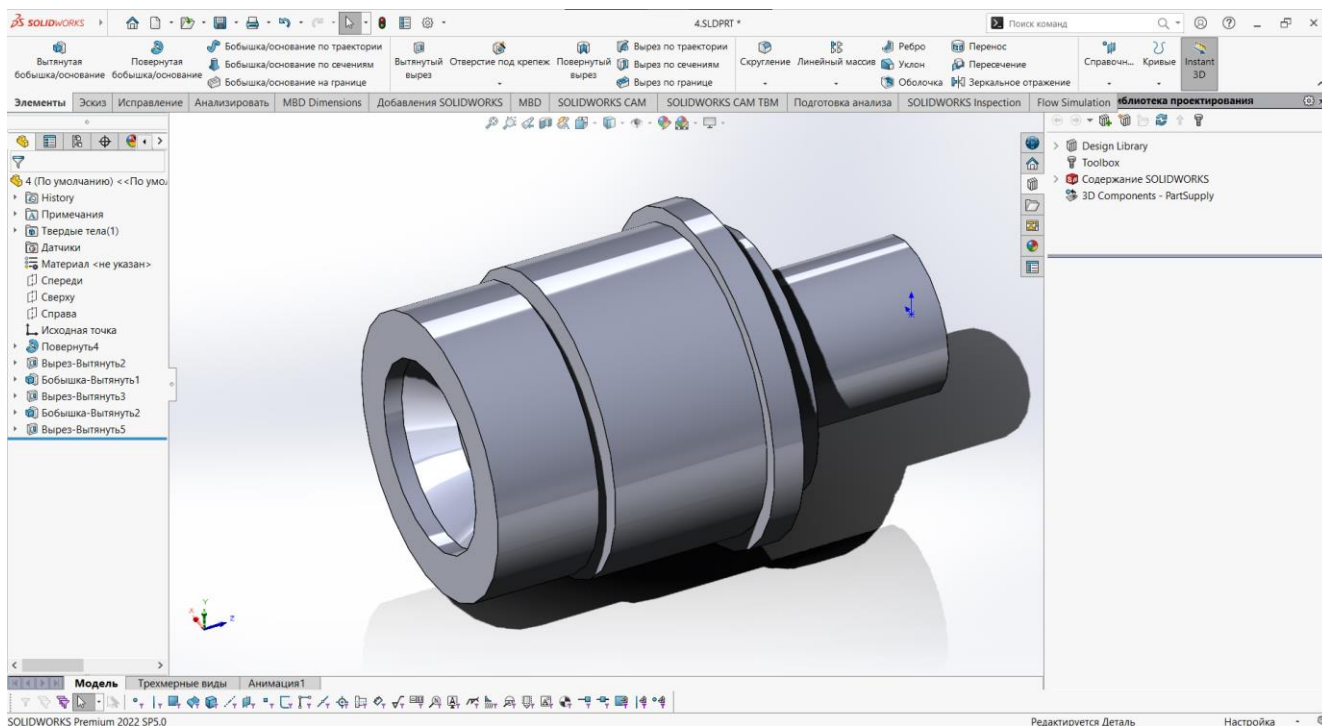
3D-модель базової конструкції формуючої головки
